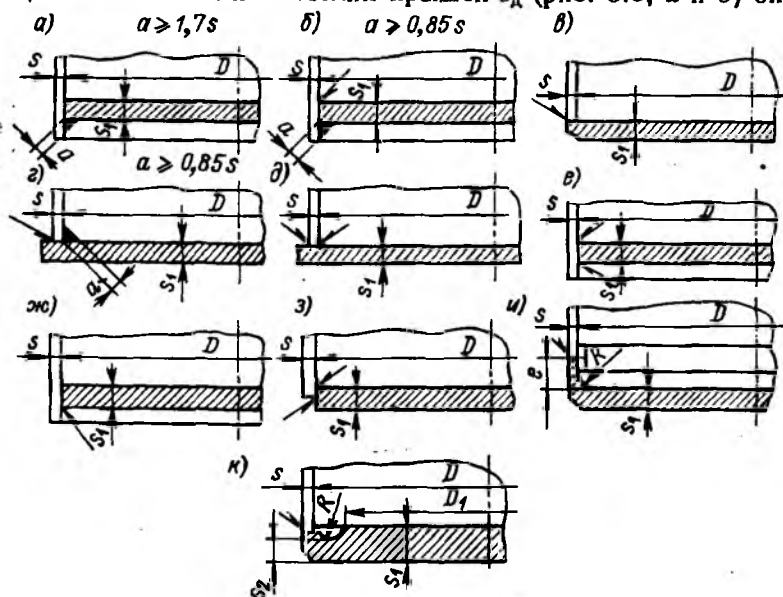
Конструкции сварных соединений плоских днищ с цилиндрическими обечайками аппаратов: а — с односторонним угловым швом без скоса кромки; б, г, з — с двусторонним угловым швом без скоса кромок; в — с односторонним угловым швом и скосом двух кромок; д — с двусторонним угловым швом и двусторонним скосом кромки обечайки; е — с двусторонним угловым швом и двусторонним скосом кромки днища; ж — с односторонним тавровым швом и криволинейным скосом кромки днища; и — с односторонним стыковым швом и подкладкой; к — с односторонним стыковым швом в замок и скосом двух кромок
